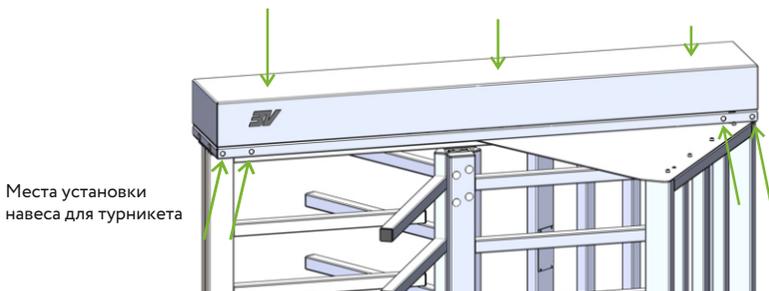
Турникет с надетой крышкой корпуса механизма
